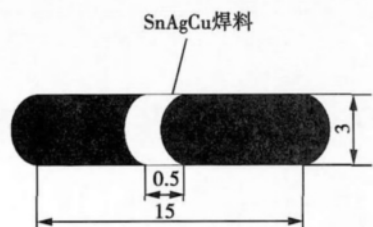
SnAgCu/Cu 钎焊接头尺寸 (mm)
